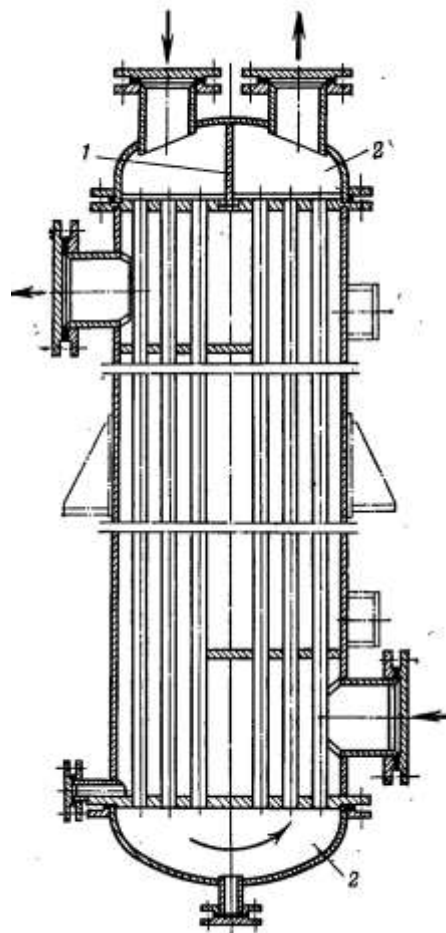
Двухходовый кожухотрубный теплообменный аппарат:
